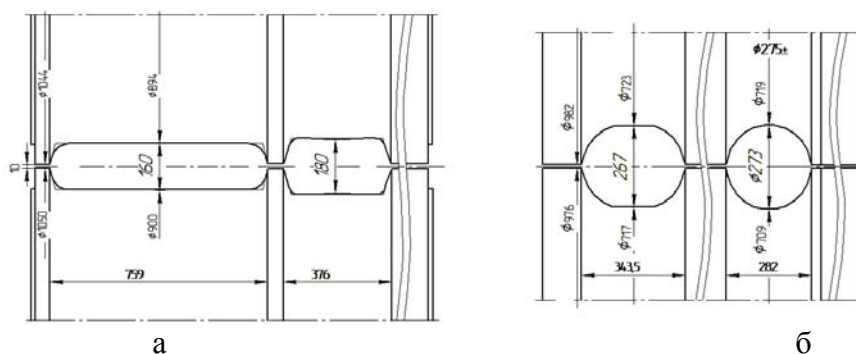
Калибровка валков в обжимной (а) и заготовочной (б) клети
